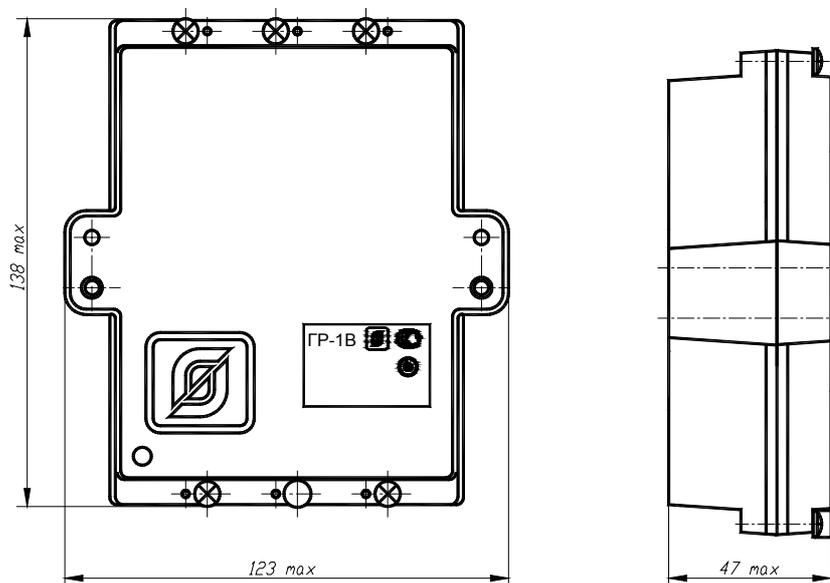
Внешний вид ГР-1В, ГР-1ВД
